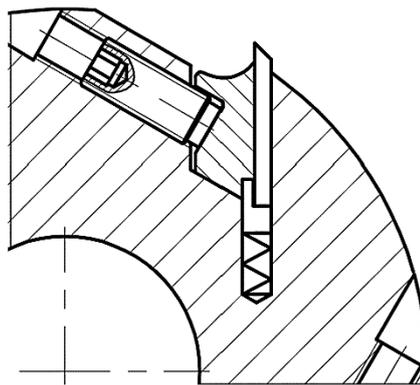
Узел крепления режущего ножа (конструкция фирмы «Leitz»)
